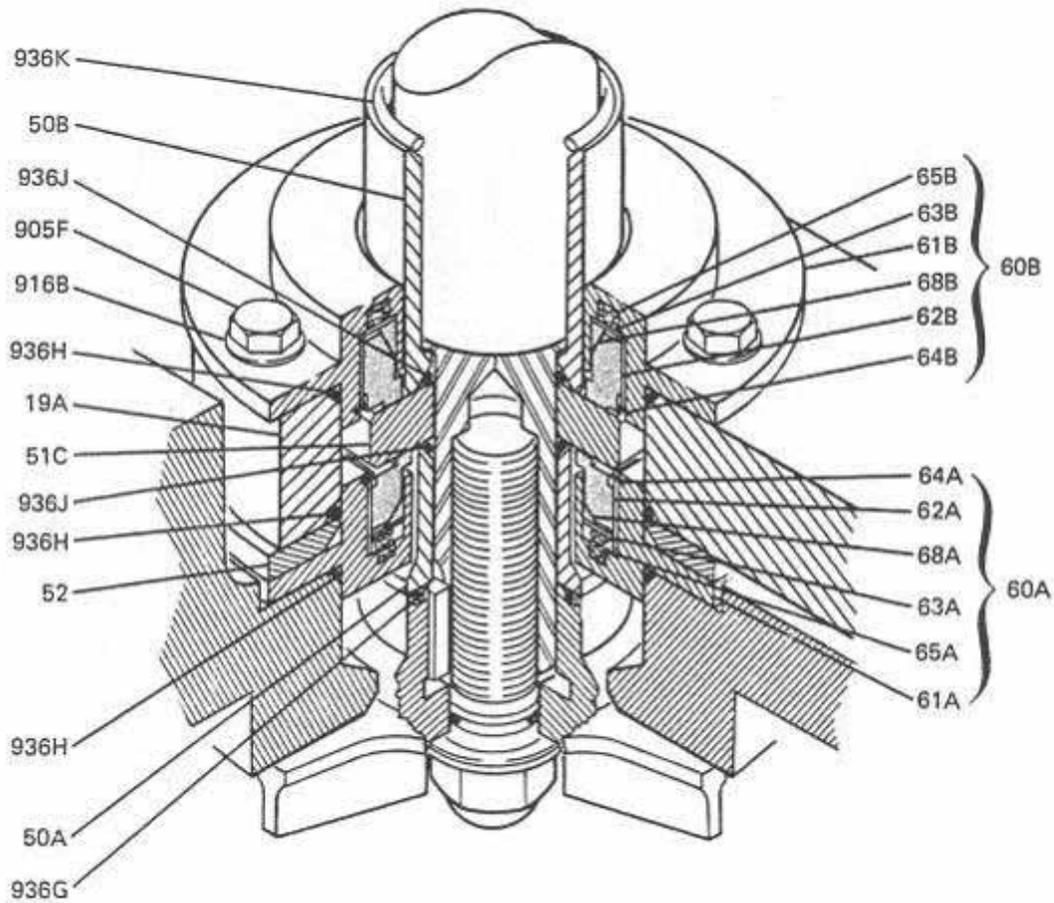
Bomba y Caja de Engranajes Disposición de Cierre Simple
